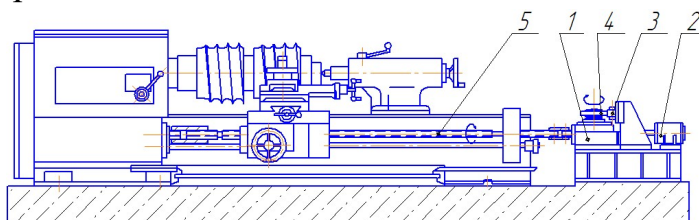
Общий вид токарно-винторезного станка оснащённым специальным копирувальным устройством
